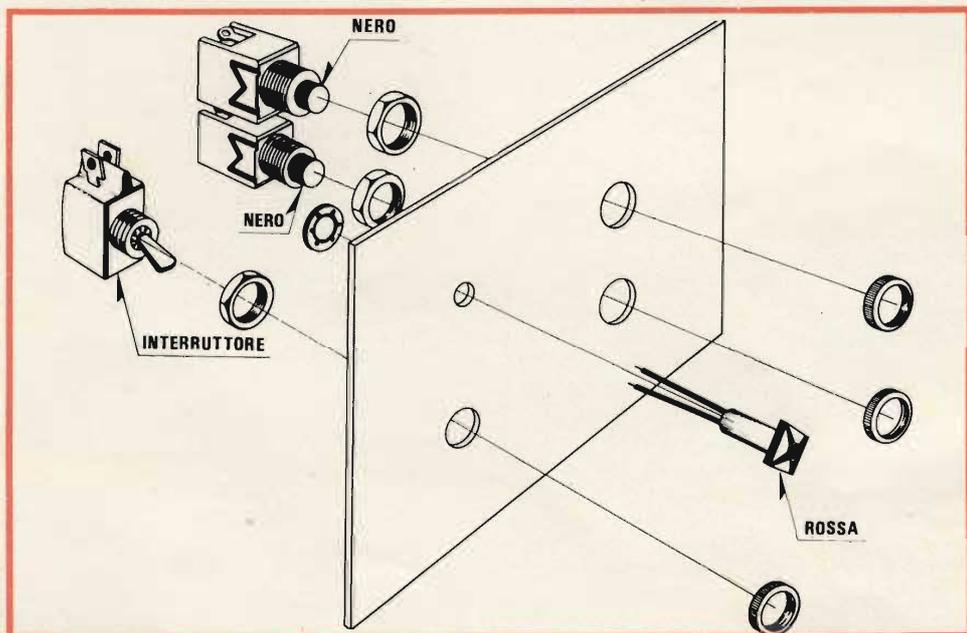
Esploso di montaggio del pannello frontale dell'alimentatore UK 660.
